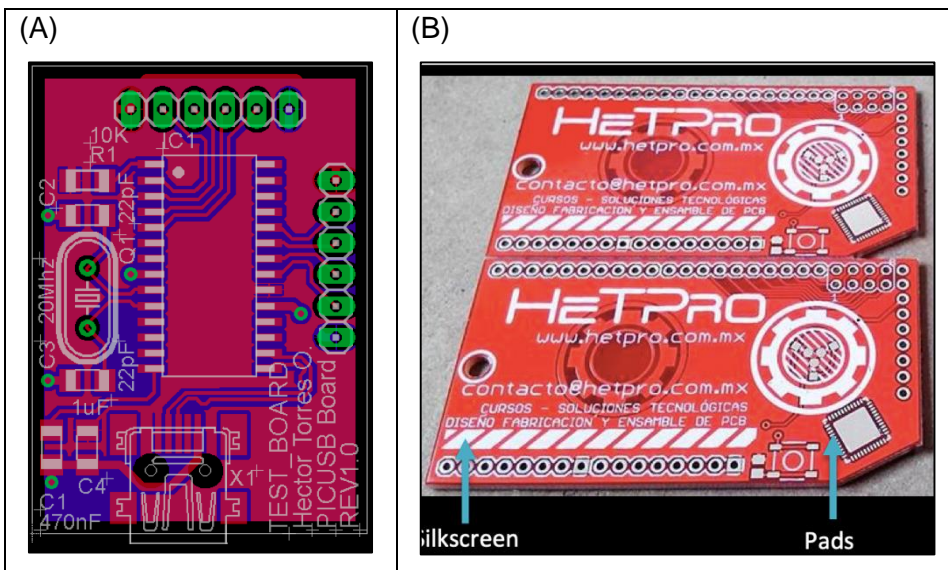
Layout terminado y placa PCB impresa, A) Circuito digitalizado, B) Circuito físico.
